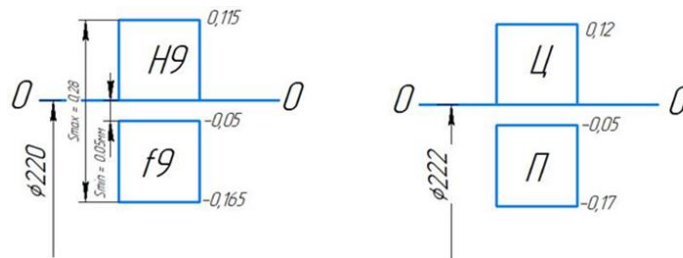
Поля допусков для отверстия в цилиндре и поршня новых деталей (а) и при переводе в ремонтный размер (б). Ц-цилиндр, П-поршень
